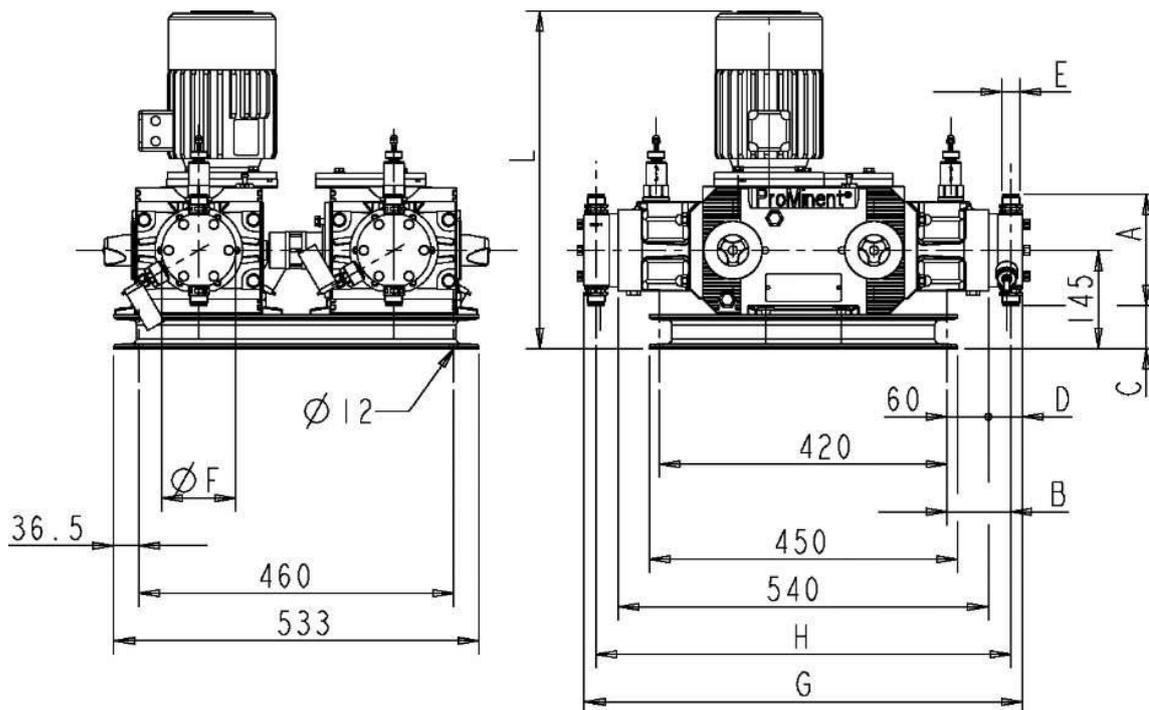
Габаритный чертеж Hydro HP3 с дополнительным насосом, двухголовочная версия (HP3а F + HP3а B). Размеры в мм.
